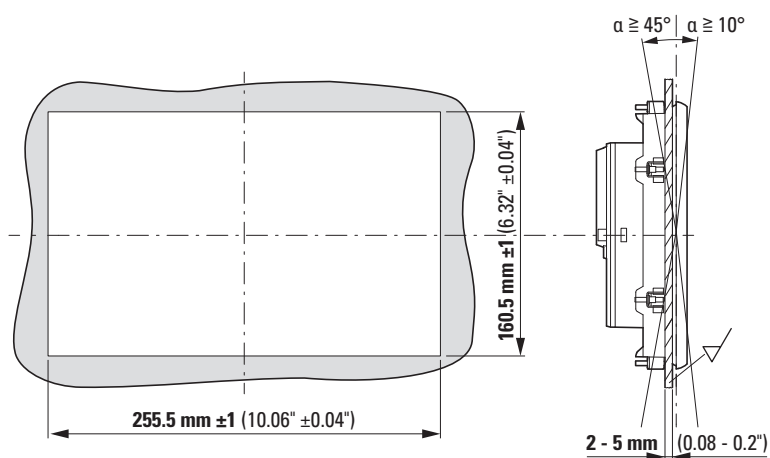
Einbauausschnitt 10.1" Front-Einbau-Geräte in mm (Inch)
